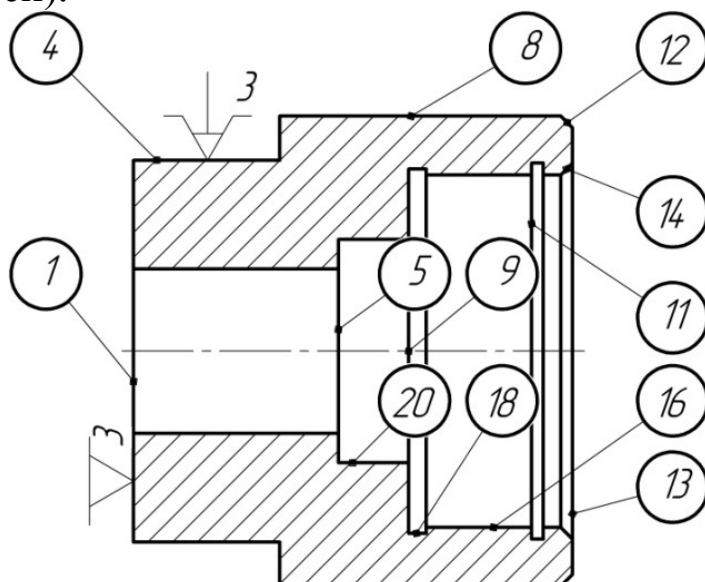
Схема базирования заготовки на установе Б операции 005
